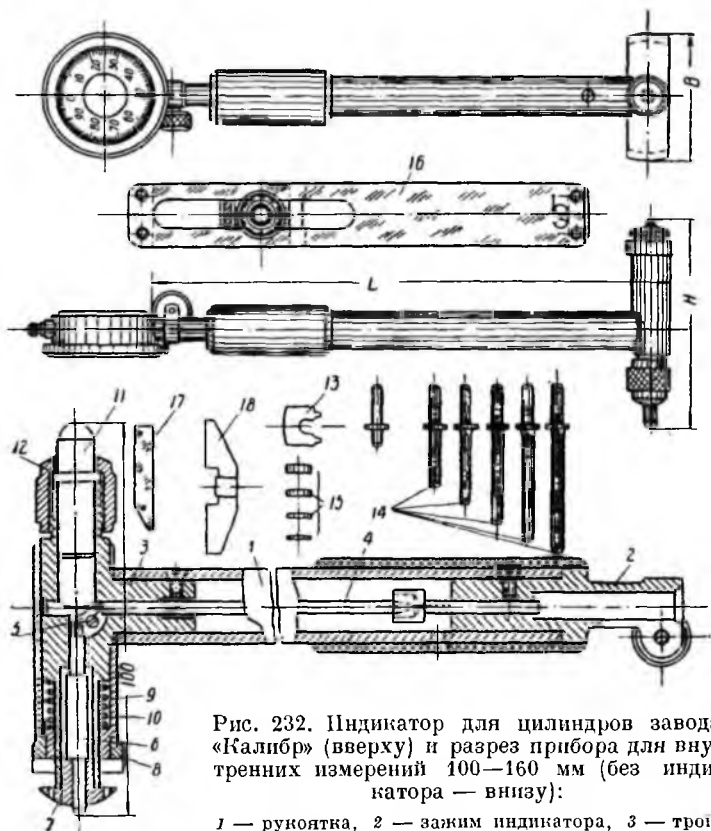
Индикатор для цилиндров завода «Калибр» (вверху) и разрез прибора для внутренних измерений 100—160 мм (без индикатора — внизу):
